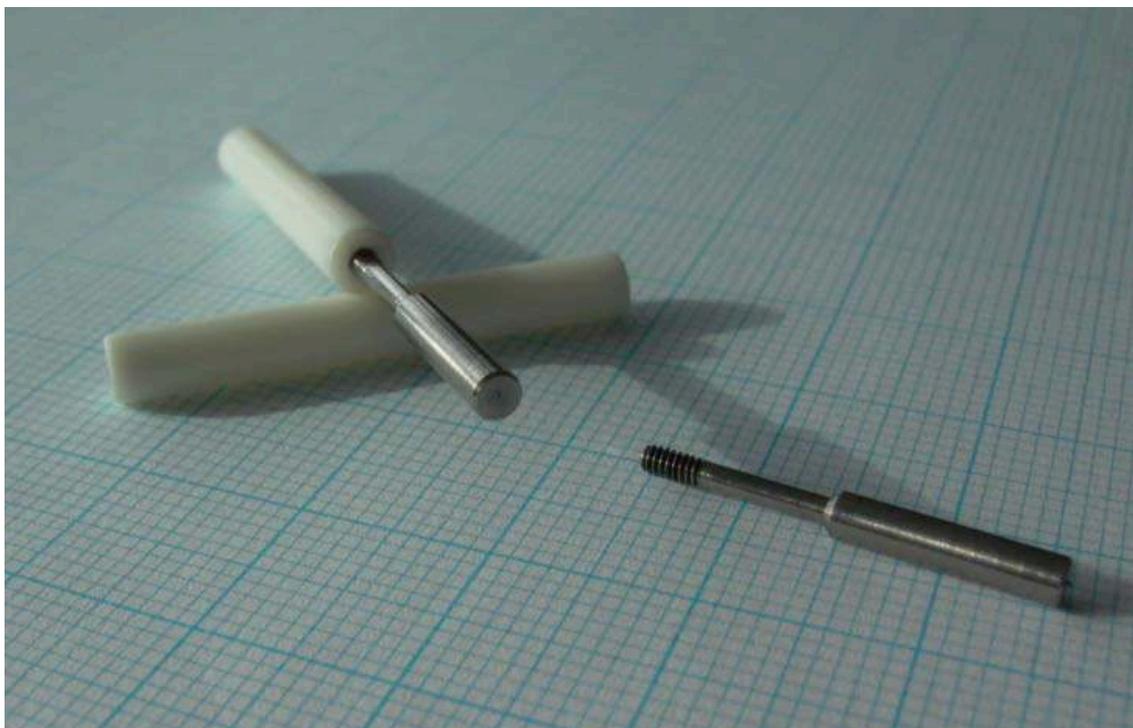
Gewindehülse in ZrO₂ mit Innengewinde M 1,6
